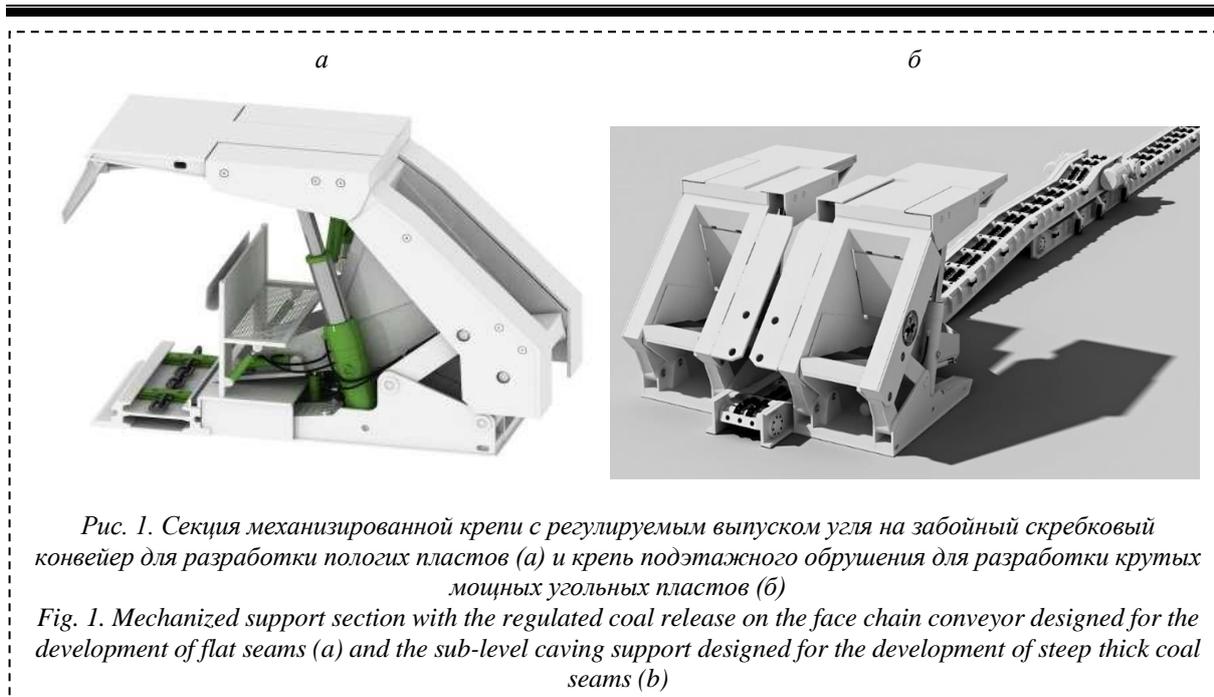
Секция механизированной крепи с регулируемым выпуском угля на забойный скребковый конвейер для разработки пологих пластов (а) и крепь подэтажного обрушения для разработки крутых мощных угольных пластов (б)
